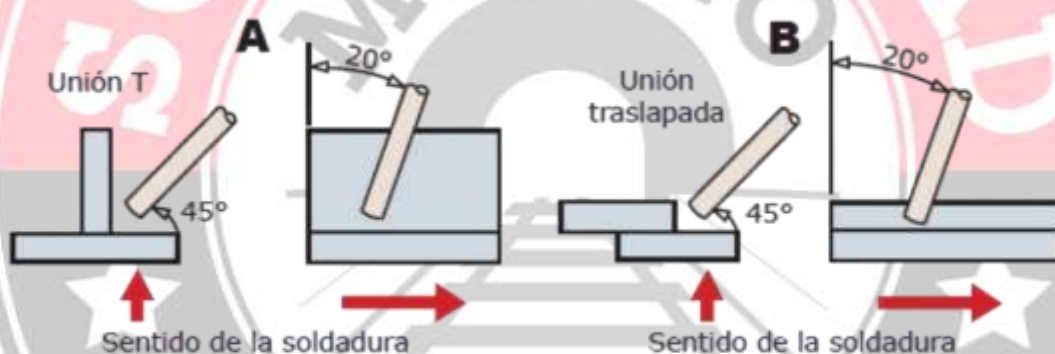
Ángulos de los electrodos para soldadura de filete
